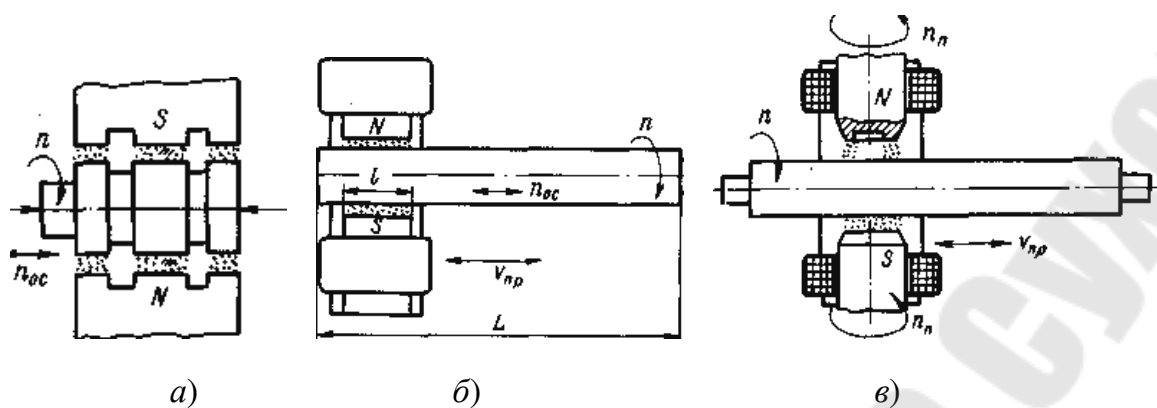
Схемы обработки прерывистых (а) и длинномерных цилиндрических поверхностей с неподвижными (б) и вращающимися (в) полюсниками
